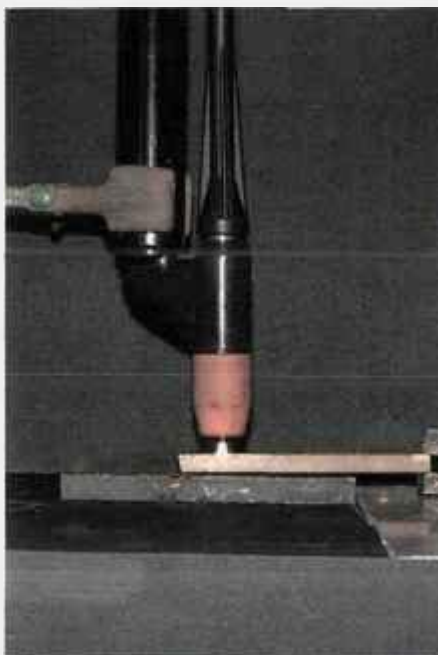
Máquina de solda plasma, marca Secheron Soudure S. A., modelo plasmafix 50E, detalhe da tocha de solda.
